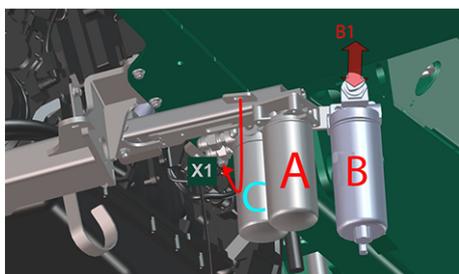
Poignée de pompe sur le préfiltre à carburant
